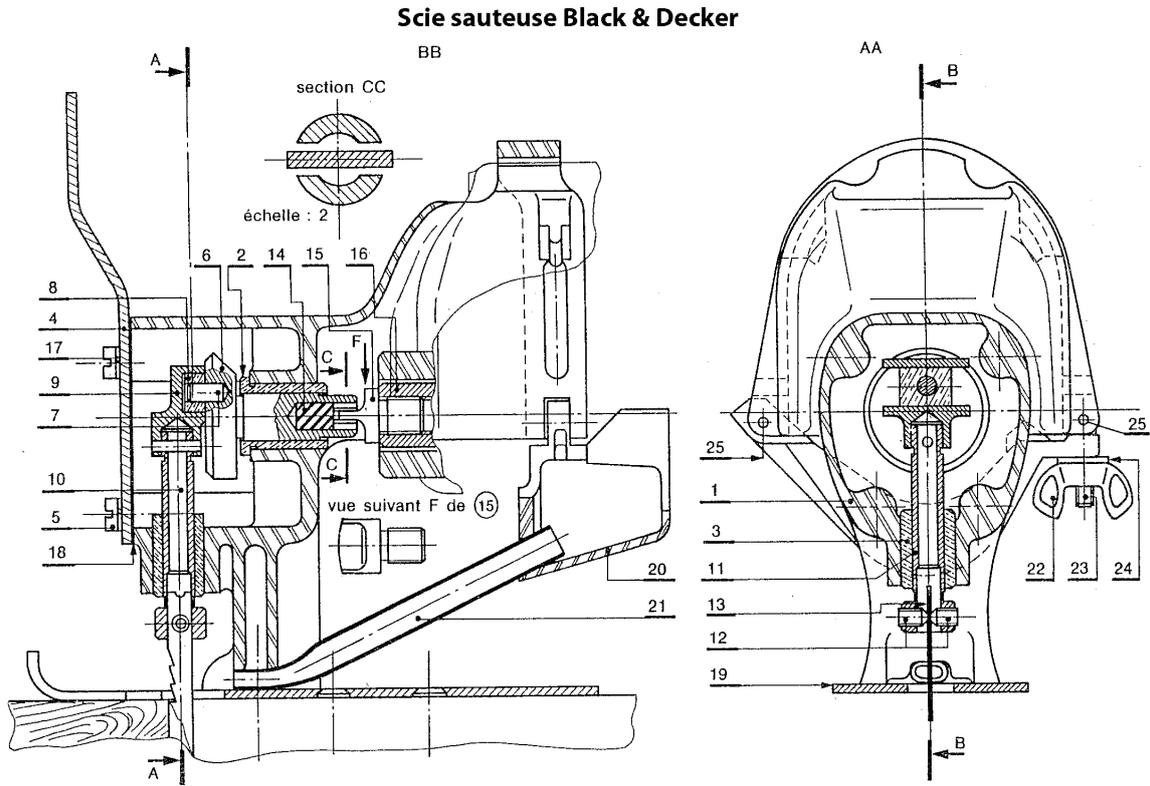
Dessin d'ensemble d'une scie sauteuse Black&Decker.
